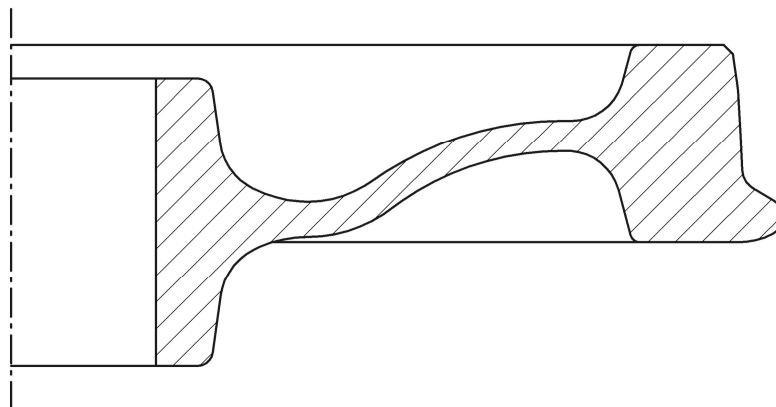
Профиль низконапряжённой конструкции цельнокатаного вагонного колеса
